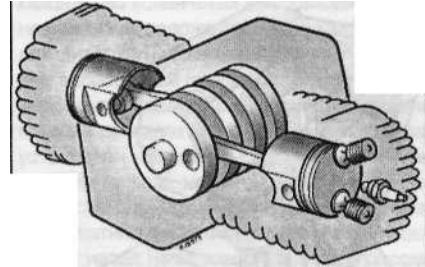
д Четырехтактный двухцилиндровый оппозитный двигатель
